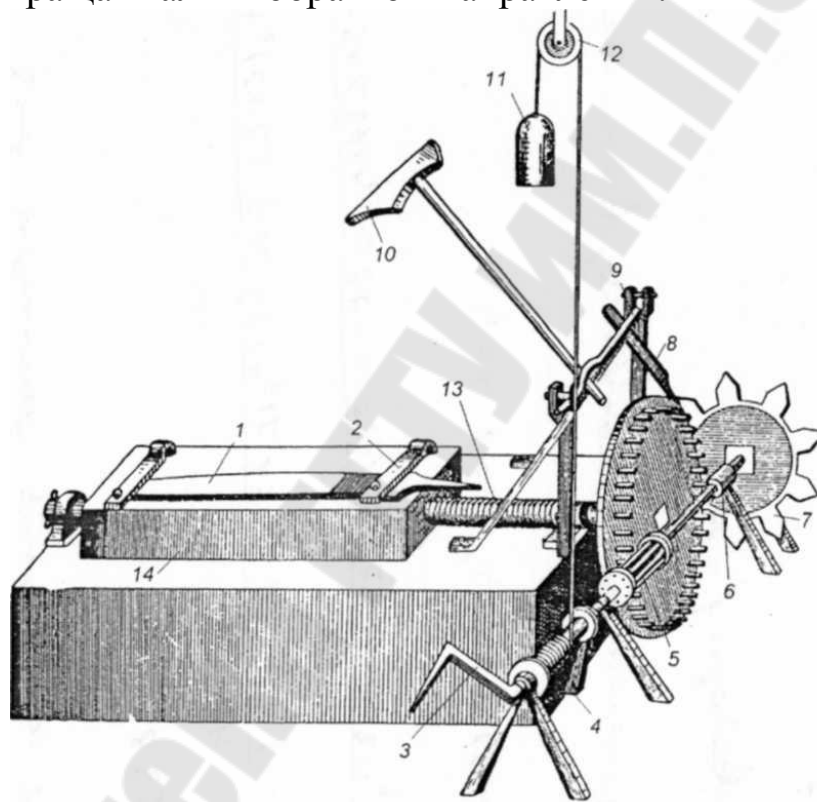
Реконструкция рисунка Леонардо да Винчи станка для насечки напильников:
